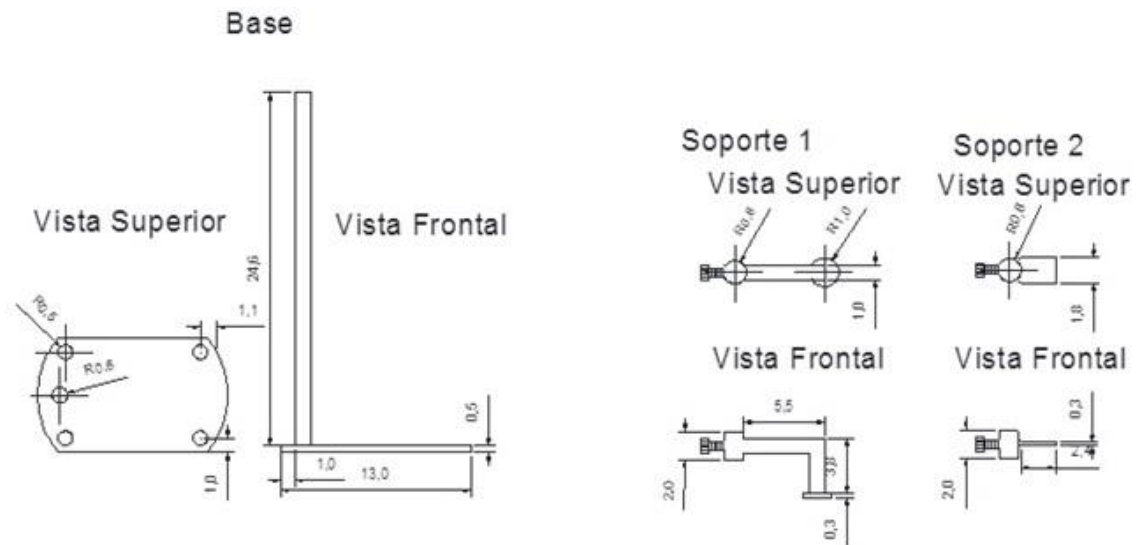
Figura E. Planos con vista frontal y superior de la estructura metálica Elaborado por: John Almache, Edwin Andrango.
